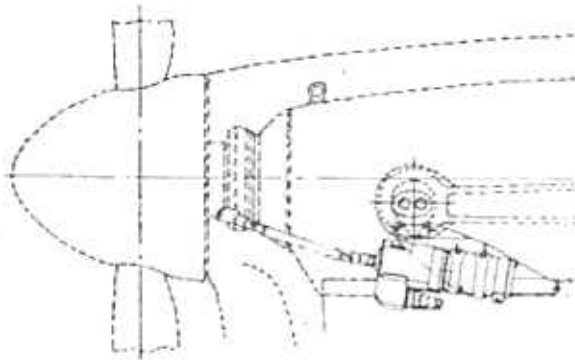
Umístění stavěcího ústrojí na motorech M 332 a M 337
